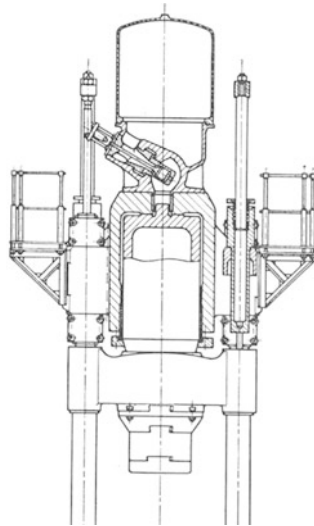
Schnitt durch den Zylinderholm der Schmiedepresse Abb. 31.
